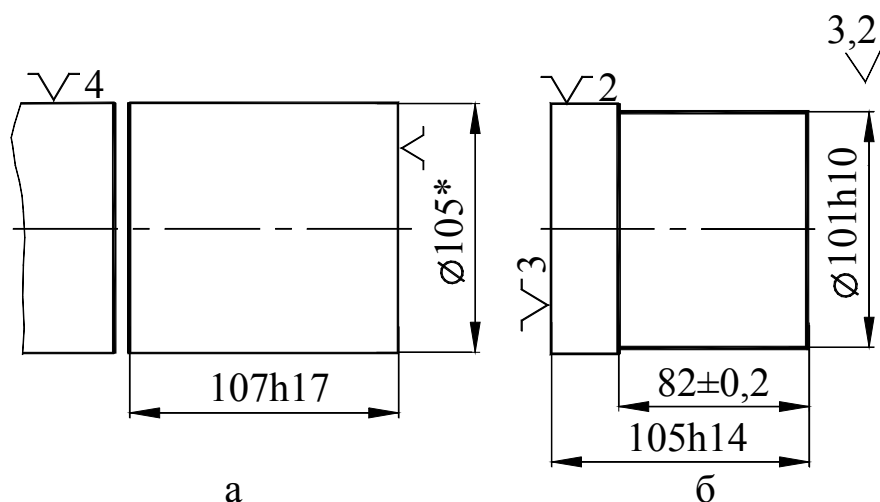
Черновые операции технологического процесса: а – заготовительная операция; б – подготовка баз для станка с ЧПУ
